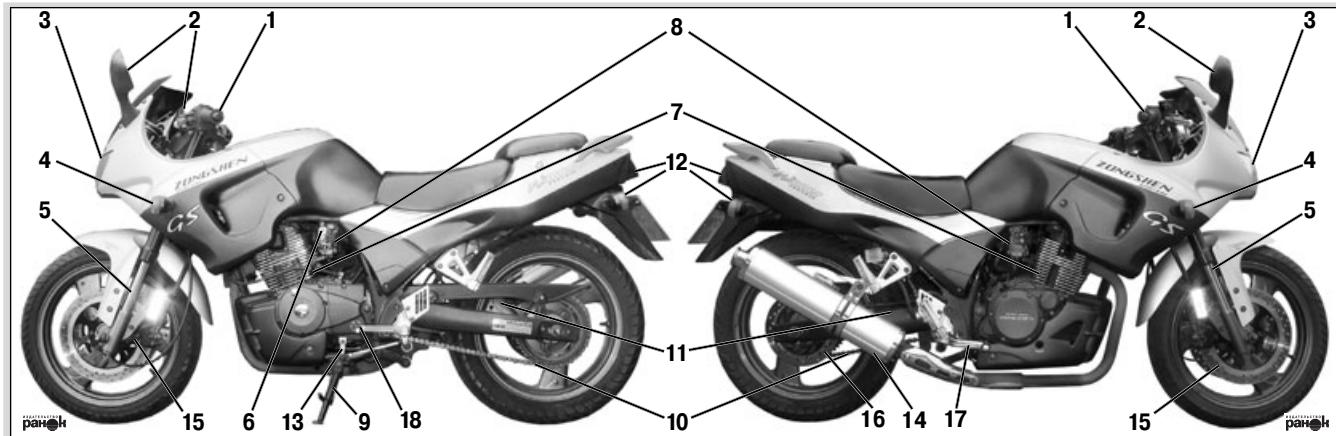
Конструкция мотоцикла: 1 – руль; 2 – зеркало заднего вида; 3 – фара головного света; 4 – передний указатель поворотов; 5 – передний амортизатор; 6 – топливный кран; 7 – двигатель; 8 – карбюратор; 9 – боковая и опорная стойки; 10 – приводная цепь; 11 – задний амортизатор; 12 – задний фонарь и задний указатель поворотов; 13 – рычаг переключения передач; 14 – глушитель; 15 – передний дисковый тормоз; 16 – задний барабанный тормоз; 17 – педаль тормоза заднего колеса; 18 – рычаг кикстартера
